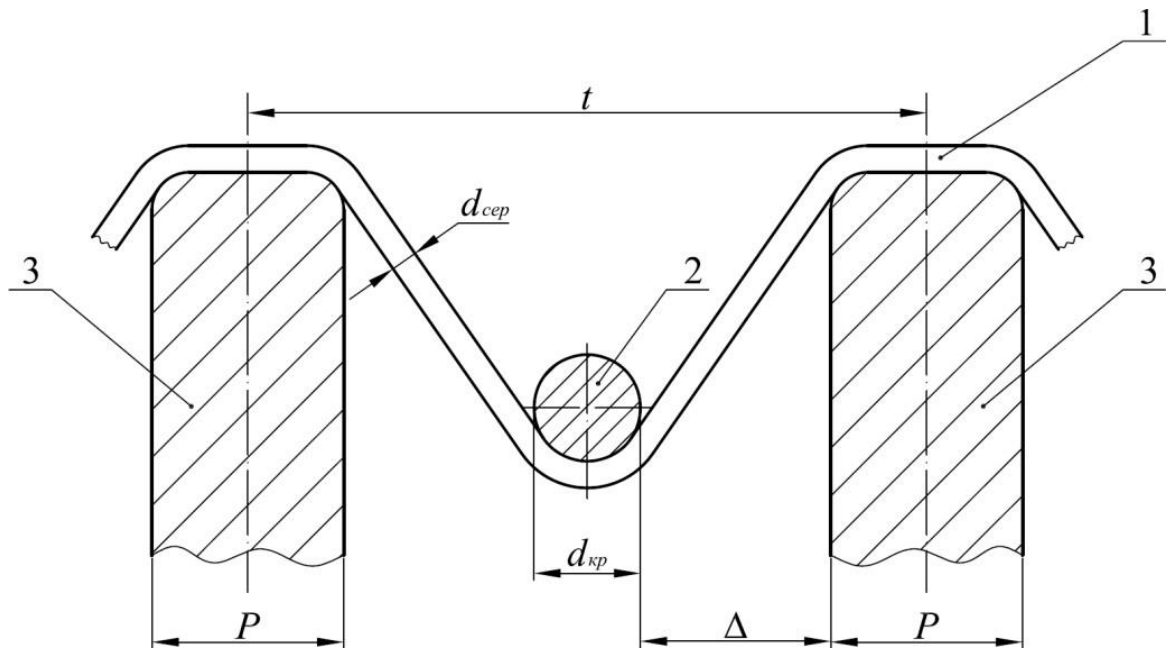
Розрахункова схема визначення величини проміжку Δ для нитки: 1 – нитка; 2 – язичкова голка; 3 – платина.
